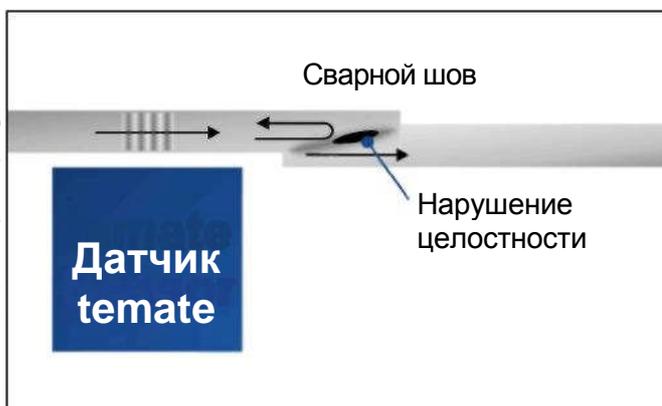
Ультразвуковой метод EMAT контроля сварки с раздавливанием шва.
